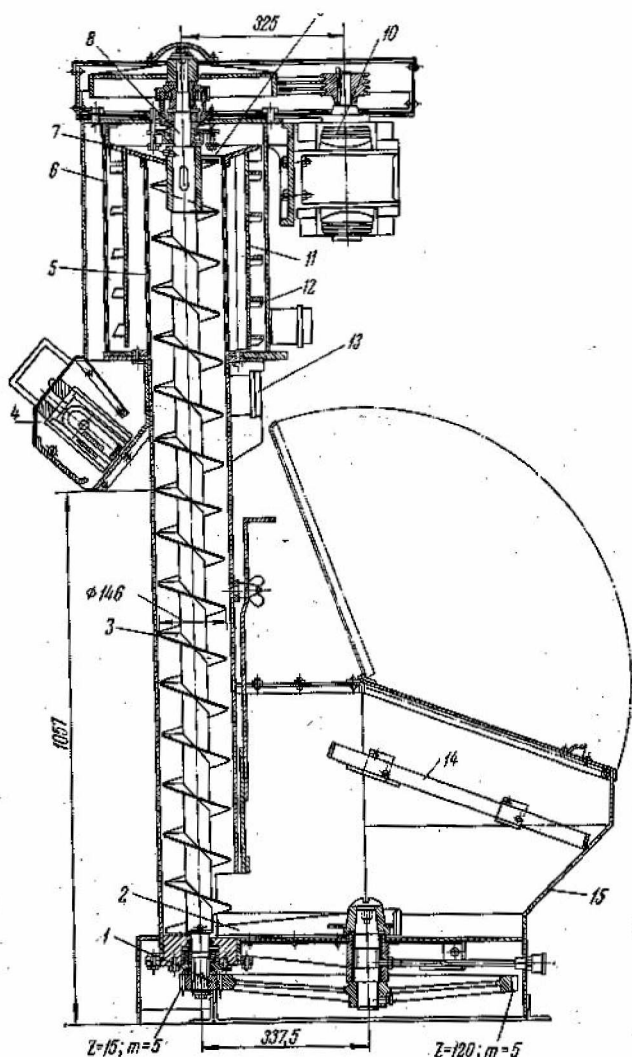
Просіювач ПП: 1 - зубчата передача; 2 - спіральна лопать; 3 - шнек; 4 - постійні магніти; 5 - сито внутрішнє; 6 - сито зовнішнє напівциліндричне; 7 - обертовий конус; 8 - вал; 9 - отвір в конусі; 10 - привід; 11 - пластини; 12 - лопатка; 13 - збірник відходів; 14 - запобіжна решітка; 15 - завантажувальний бункер
